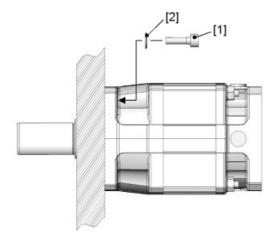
Instalação do servo-redutor planetário PS.C na máquina
